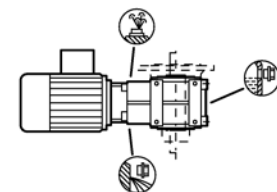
Bauformen für B.38 mit zusätzlicher Verschlusschraube
